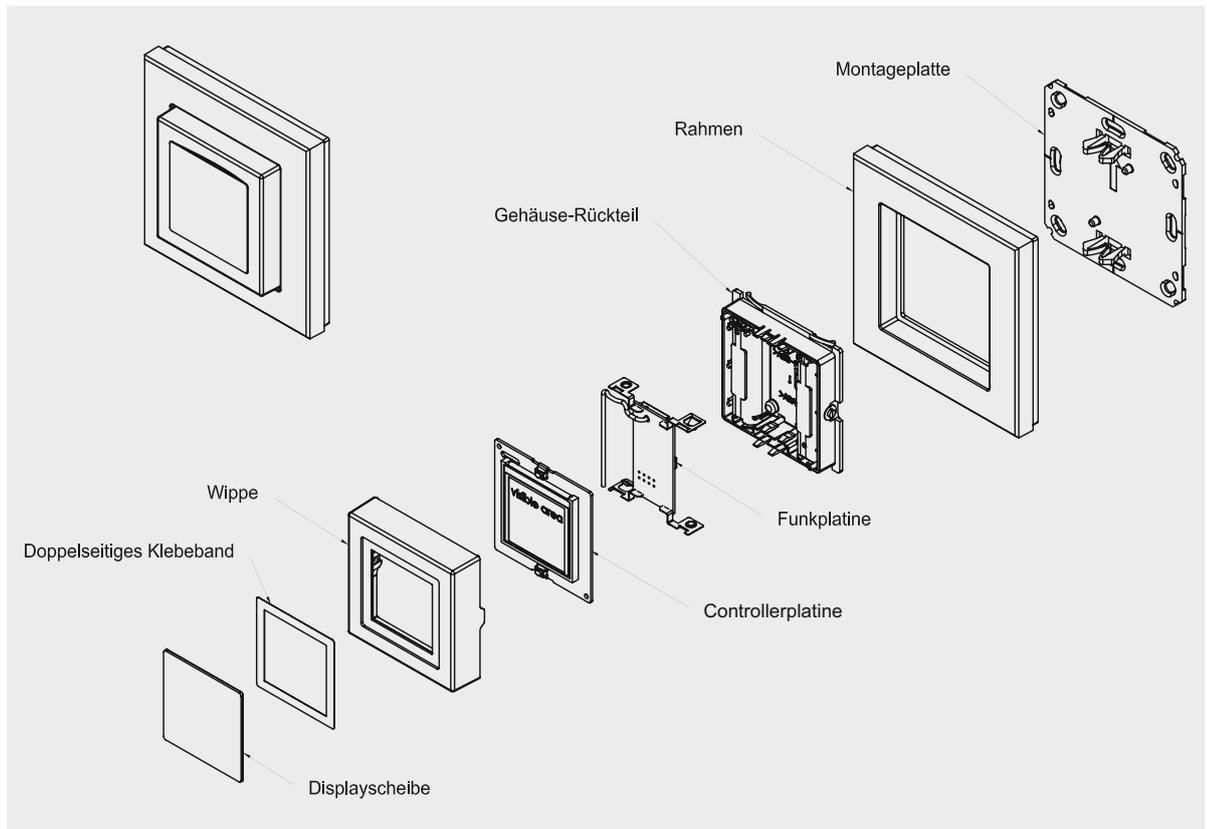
Die Explosionszeichnung gibt einen Überblick über den Gesamtaufbau des Gerätes.
